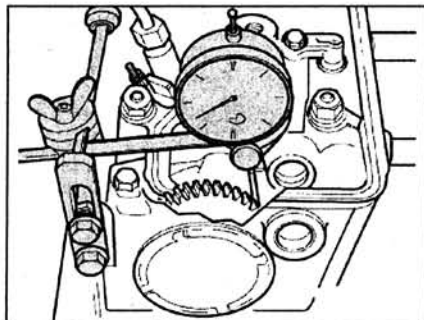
Закрепите стрелочный индикатор на головке блока цилиндров с помощью держателя VW 387.
